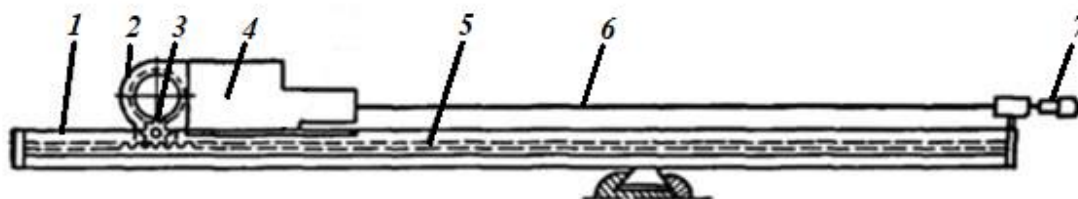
Схема зубчато-реечного привода подачи: 1 – направляющая; 2 – привод подачи (двигатель с редуктором); 3 – шестерня подачи; 4 – привод вращения; 5 – зубчатая рейка; 6 – буровой став; 7 – исполнительный орган
